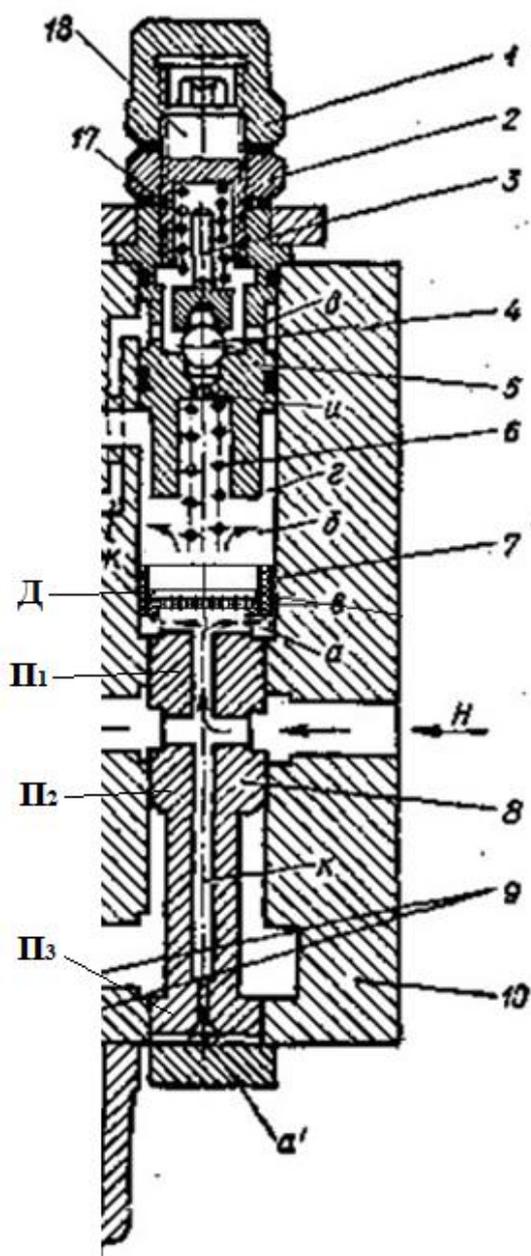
Перепускной и предохранительный (разгрузочный) клапаны гидрораспределителя гидросистемы экскаватора ЭО-2612А: Д – демпферный узел; $П_i$ – поршневые узлы; 4- шарик предохранительного клапан; 5 – корпус; 6- пружина; 7- демпферное отверстие; 8 – корпус перепускного клапана; 9 – золотники; 10 – корпус распределителя.
